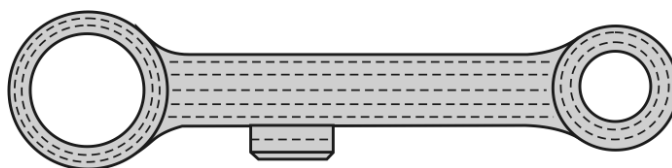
Схема сканирования подвески тормозного башмака
